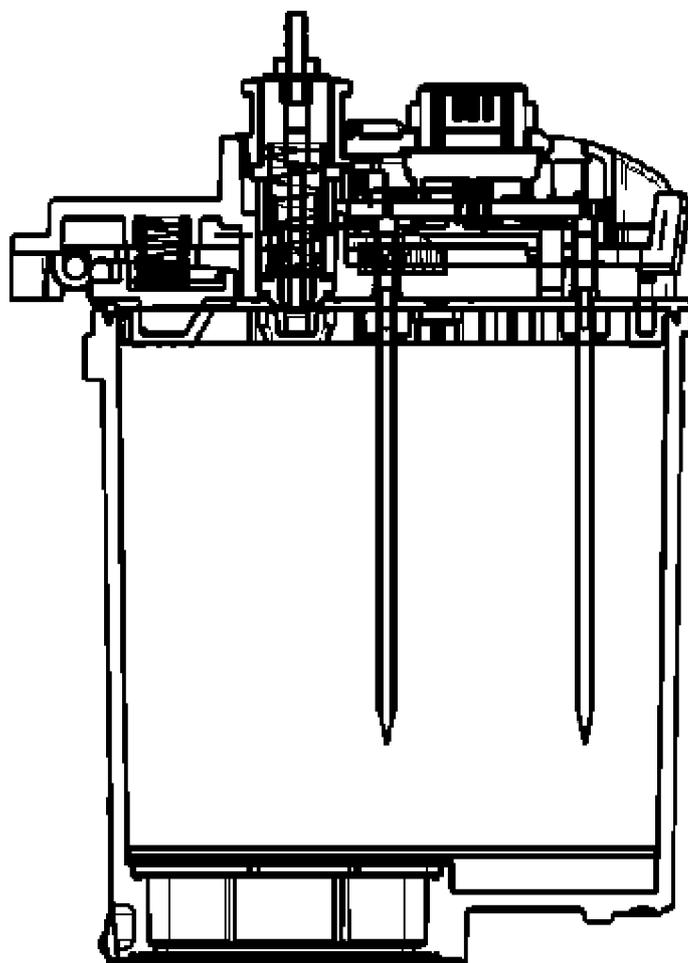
Собранный картридж с печатающей головкой: чертеж с видом в поперечном сечении
